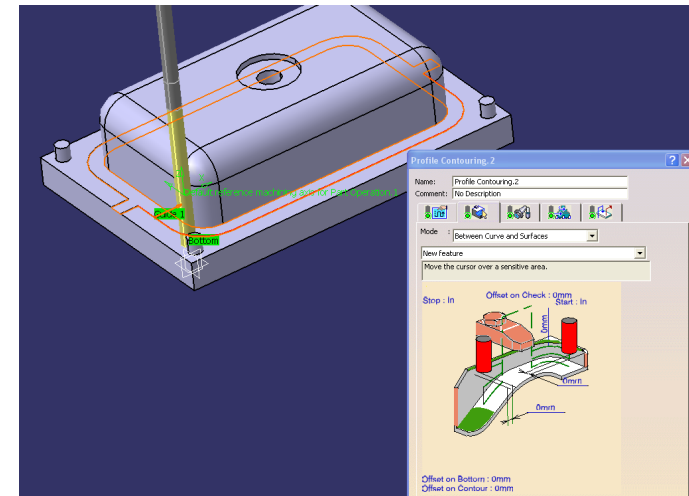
Obrobek po provedení operace Profile Contouring
